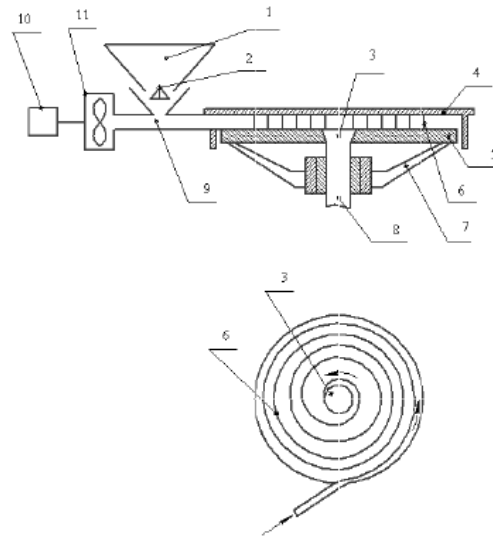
Пневматичний скарифікатор: 1 – завантажувальний бункер; 2 – запірно-дозуючий пристрій; 3 – корпус; 4 – диск; 5 – спіраль; 6 – отвір; 7 – трубопровід; 8 – кришка; 9 – електропривод; 10 – вентилятор; 11 – живильний патрубок.
